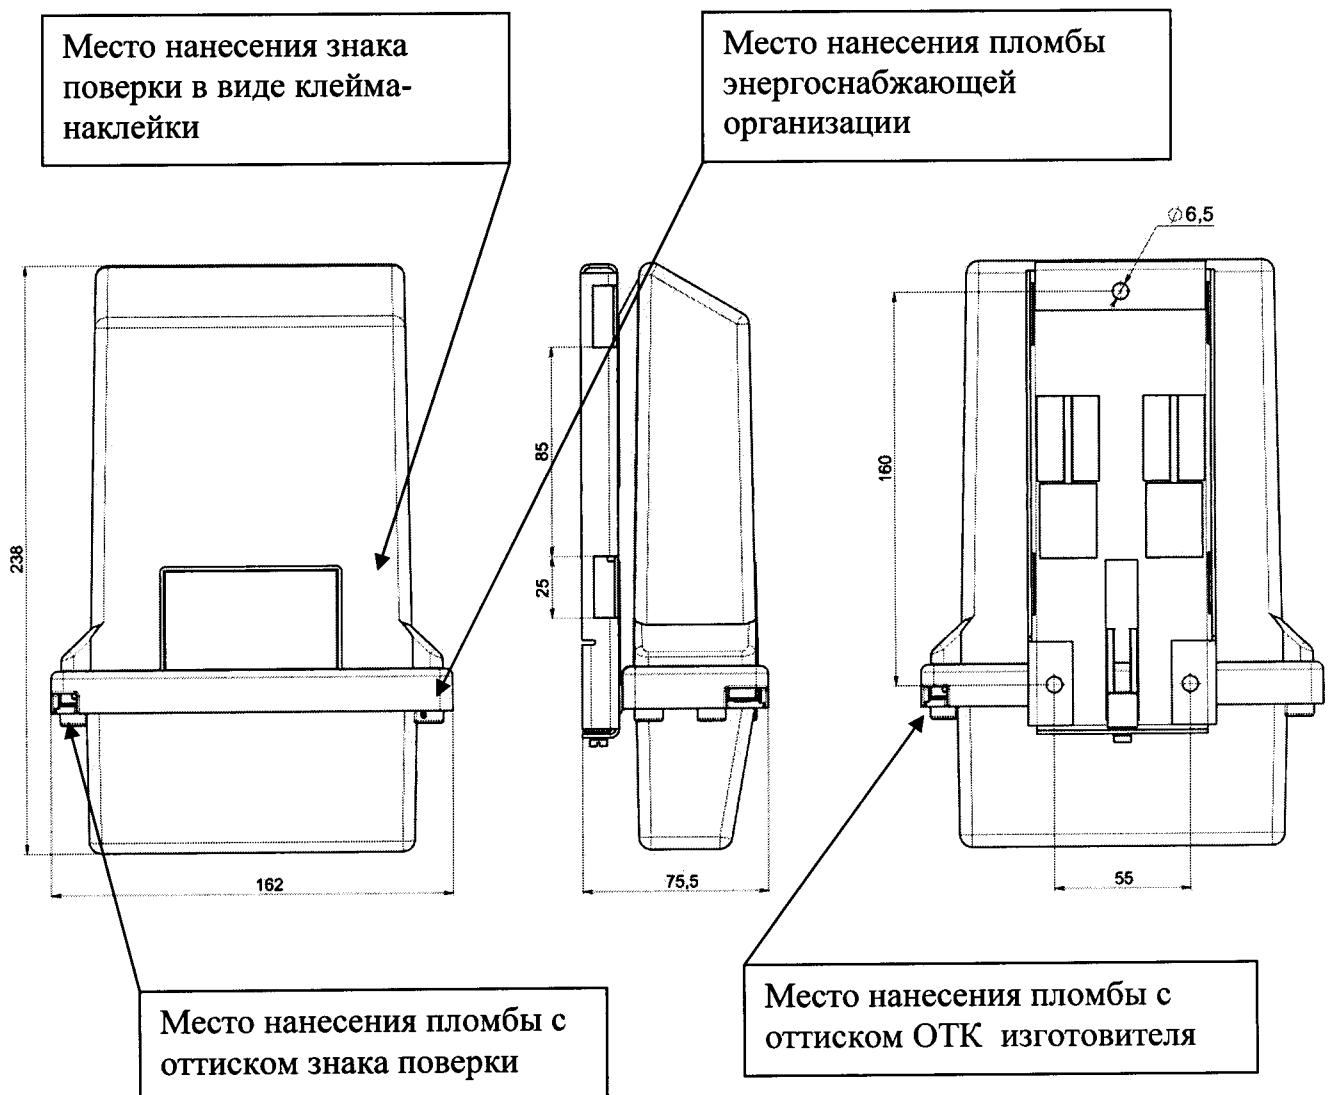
Места установки пломб и нанесения знаков поверки
